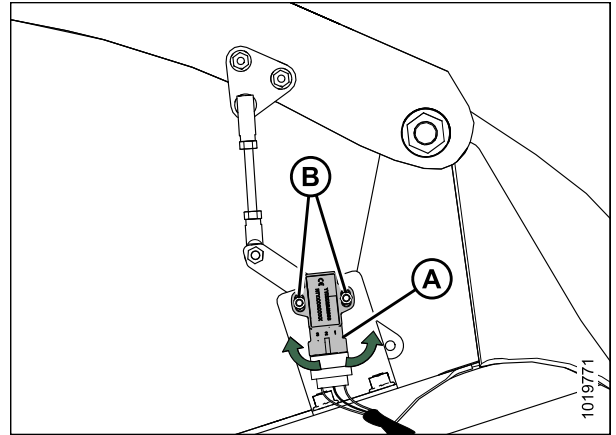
Sensor de altura del molinete – brazo derecho del molinete (molinete arriba)
